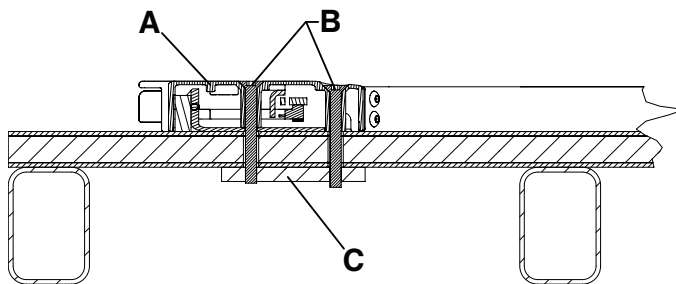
Lato piedi montato a pavimento – Vista 3A
